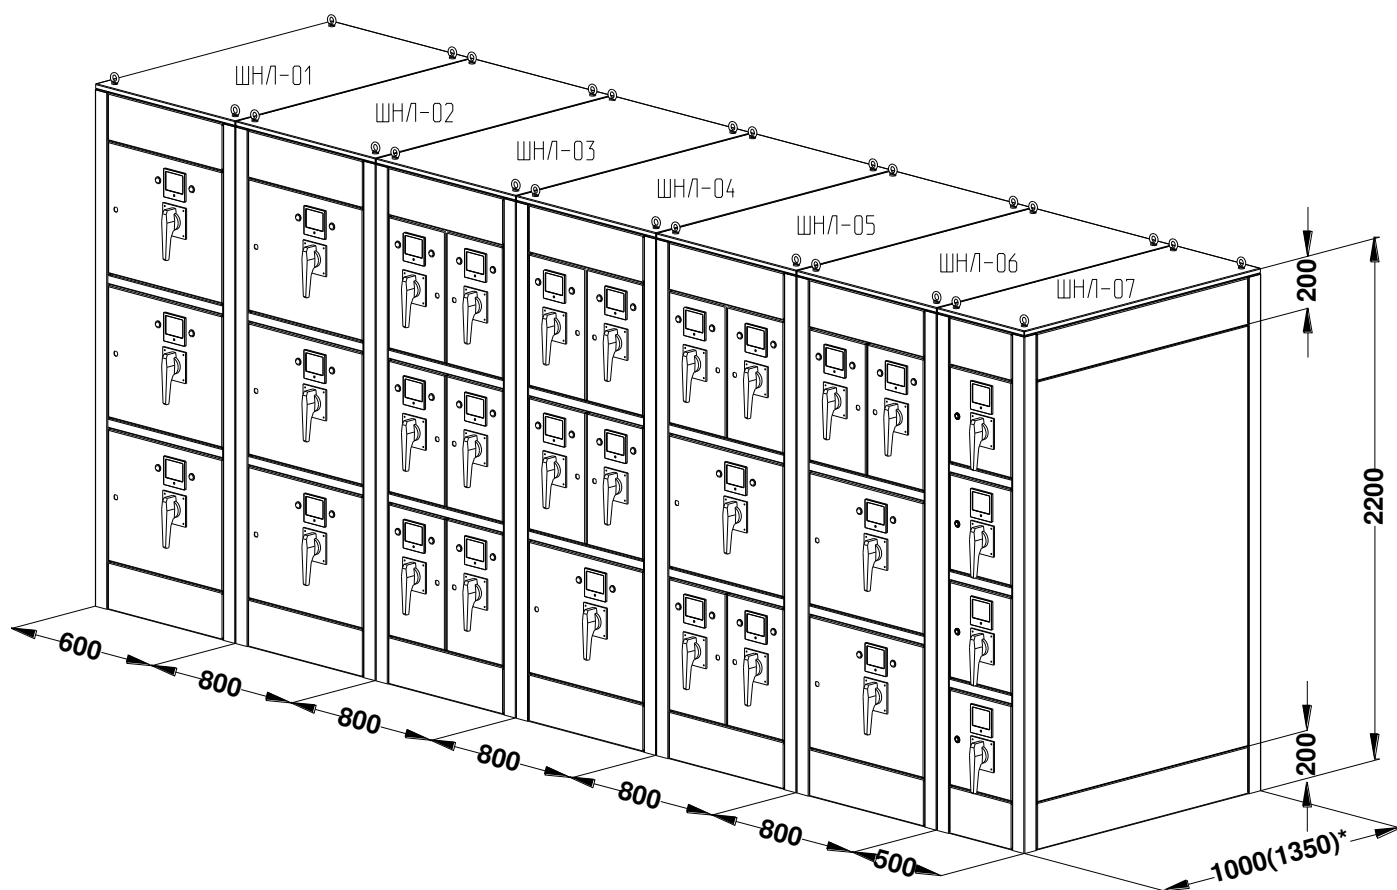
Габаритные размеры типоразмеров шкафов линейных РУНН
